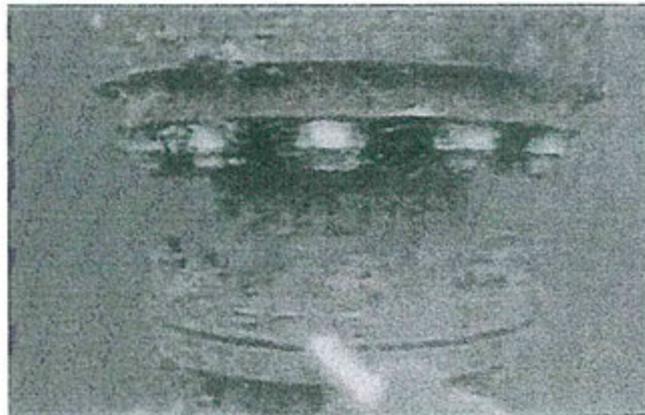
Brida de unión de manguerotes de # 10 y # 11
